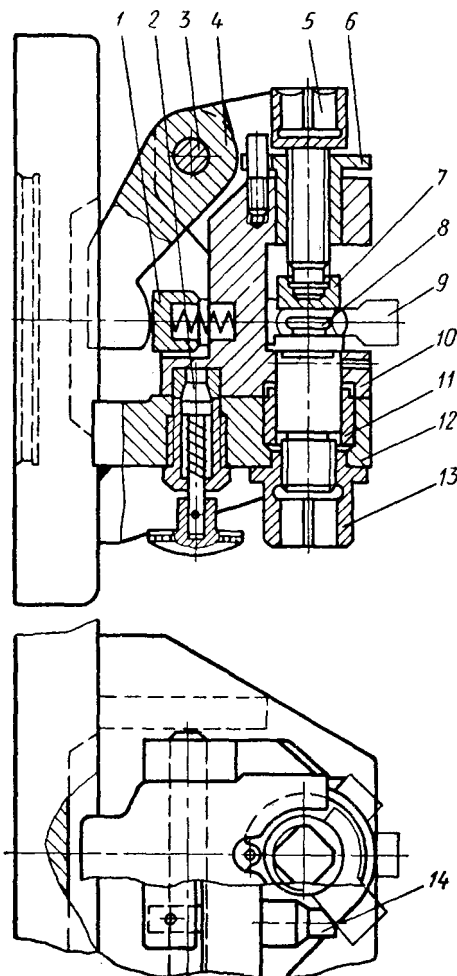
Патрон, обеспечивающий обработку отверстий тройников и крестовин с одной установки на токарных и револьверных станках
